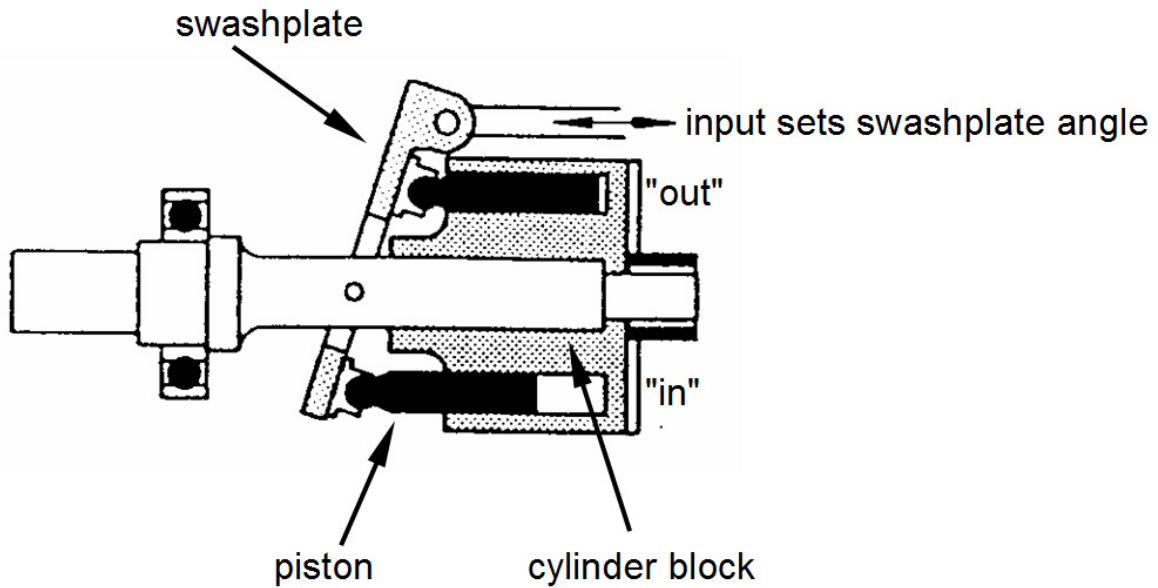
Prinzip einer Axialkolbenpumpe mit variabler Verdrängung (variable displacement axial multiple-piston pump)
